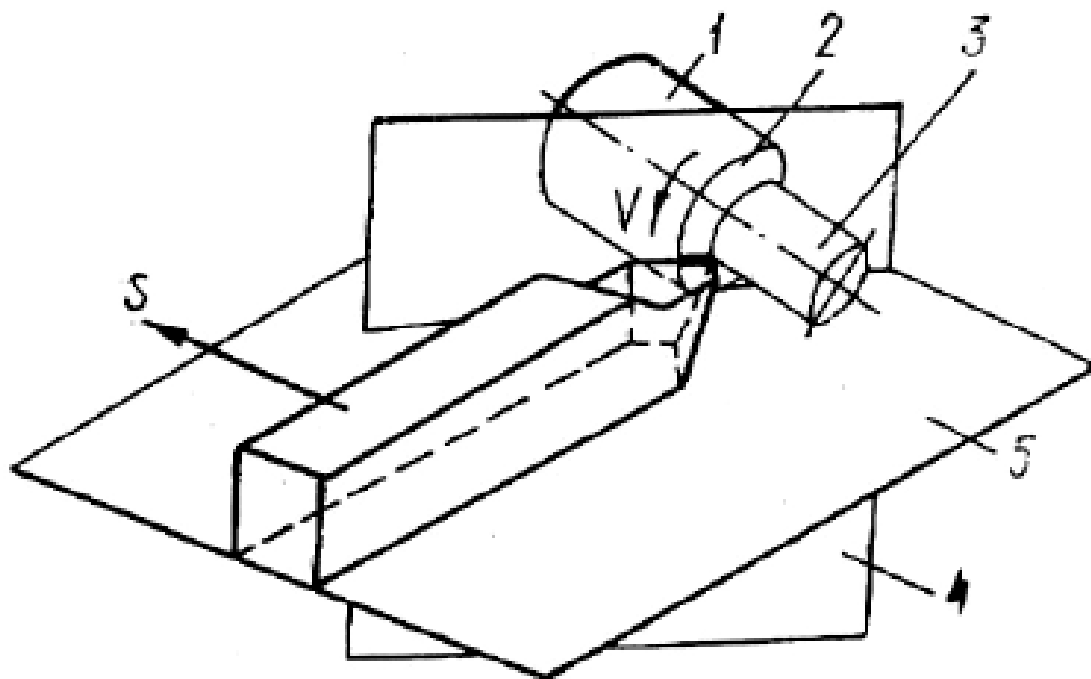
Поверхні та площини різця: 1 – оброблювана поверхня; 2 – поверхня різання (перехідна поверхня); 3 – оброблена поверхня; 4 – площина різання; 5 – основна площа
